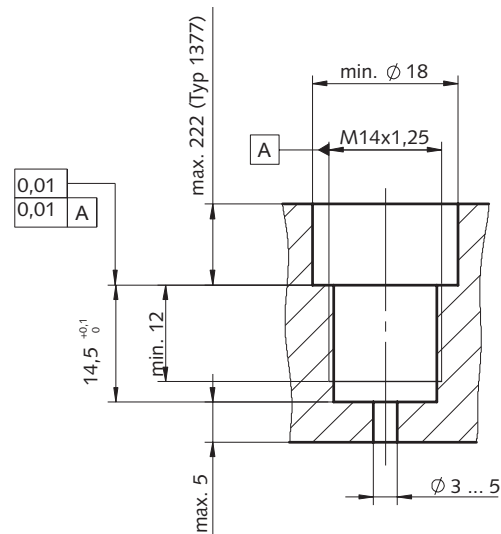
Zurückversetzt eingebauter Sensor. Bohrungsdurchmesser gemäß Montagewerkzeug
